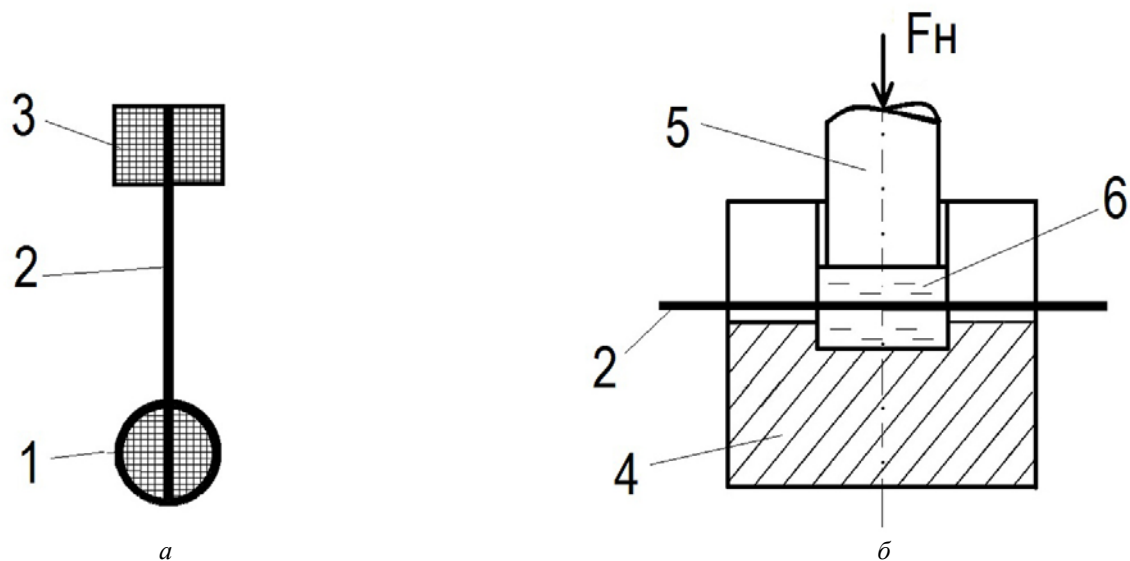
Схема экспериментального образца (а) и способа его изготовления (б), где 1 – матричный блок; 2 – армирующее волокно; 3 – крепежный блок; 4 – обогреваемая мини пресс-форма; 5 – пуансон; 6 – расплав полимера [11]
